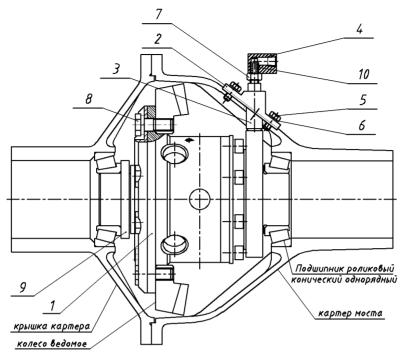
Схема дифференциала ДБП3741-2403000 с металлическим кольцом воздихоподвода
